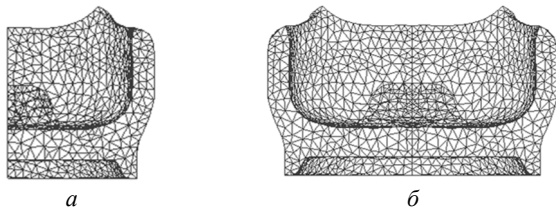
Форма торця стінки після видавлювання заготовки квадратного перерізу: *a* – четвертої частини заготовки і *б* – половини заготовки
